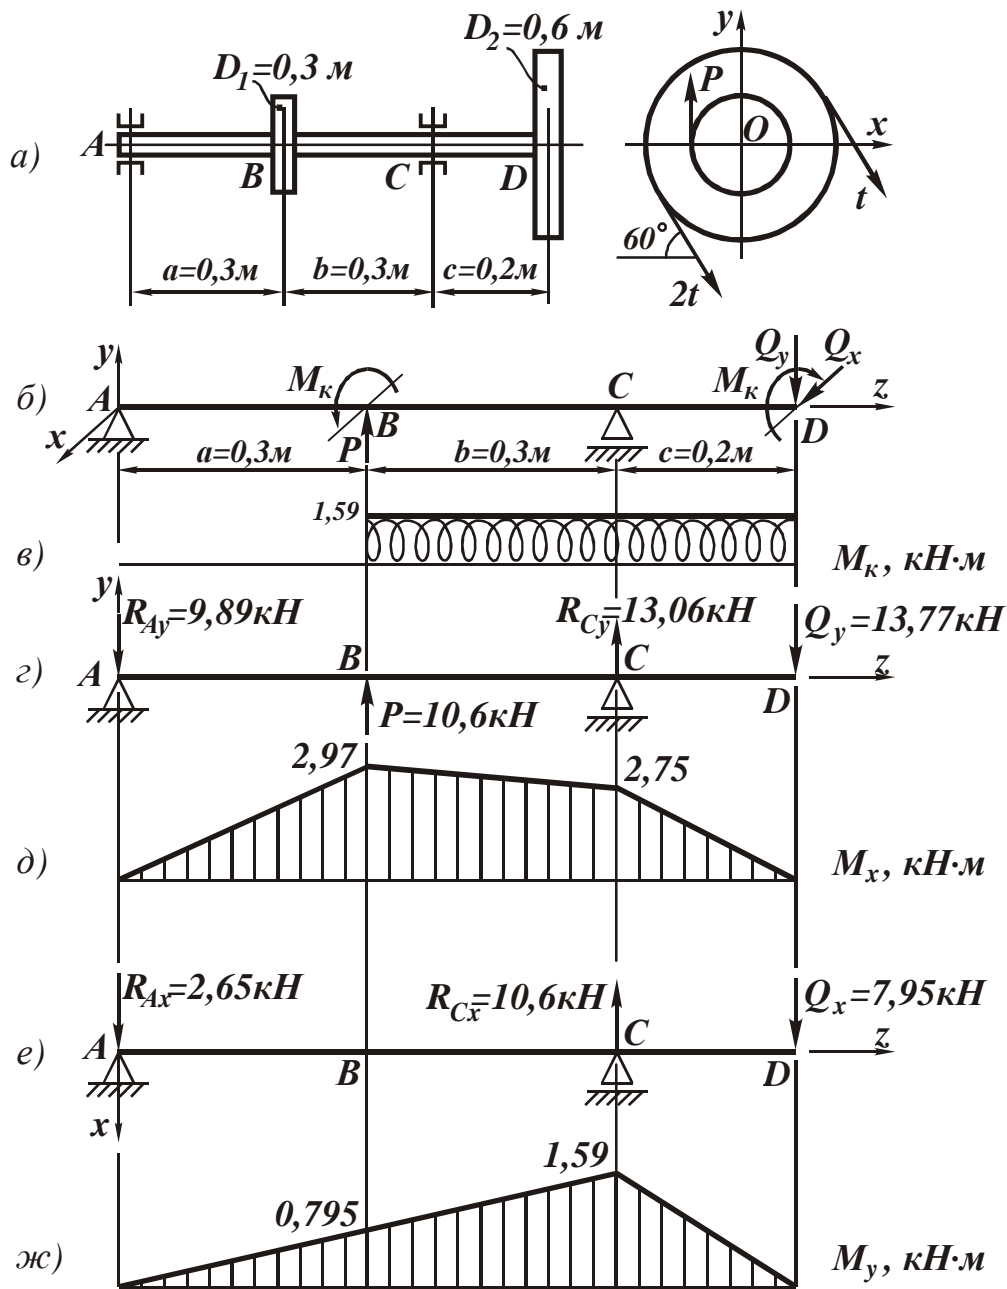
Расчётная схема и эпюры моментов внутренних усилий в поперечных сечениях вала
